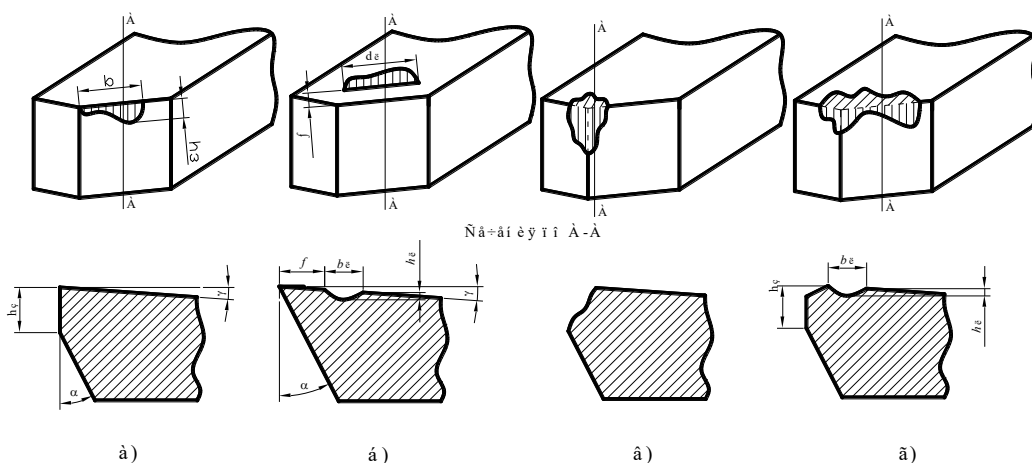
Износ режущего лезвия резца, изготовленного из быстрорежущей стали: а – неравномерный износ по задней поверхности (b_3 – ширина площадки, h_3 –
